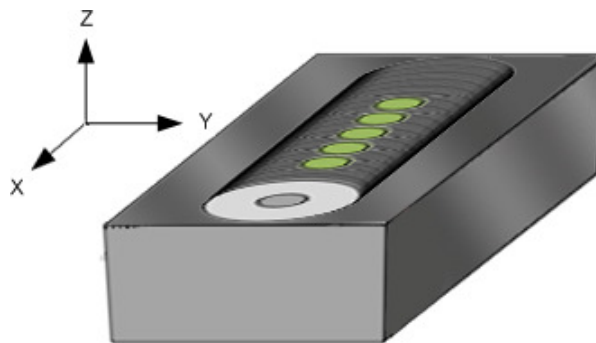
Esquema del corte para la obtención de muestras en el plano longitudinal (plano XY).
